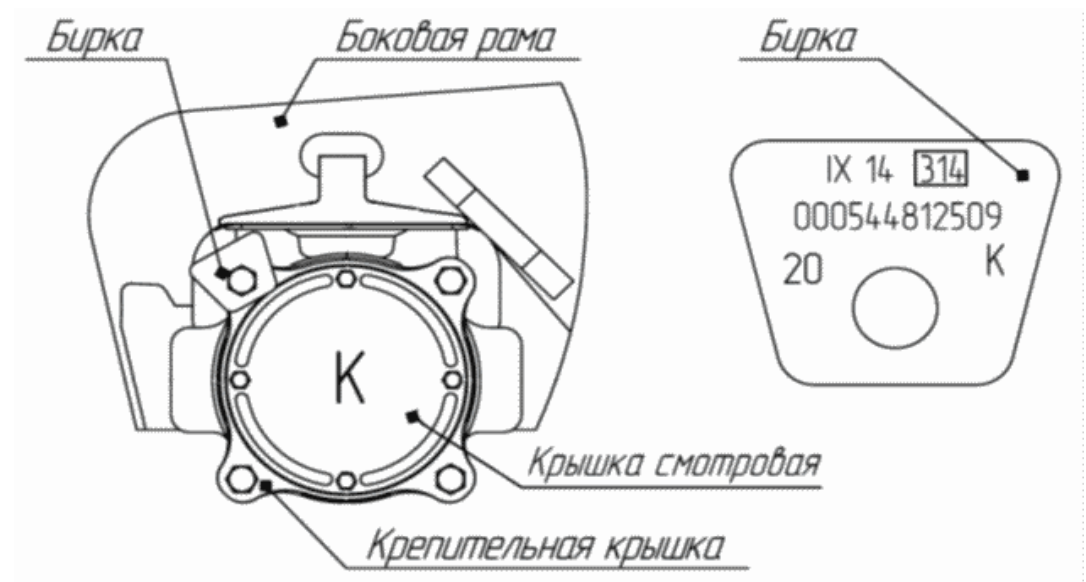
Внешние отличительные признаки буксовых узлов с подшипниками кассетного типа в габаритных размерах 130x250x160 мм торговой марки «SKF»
